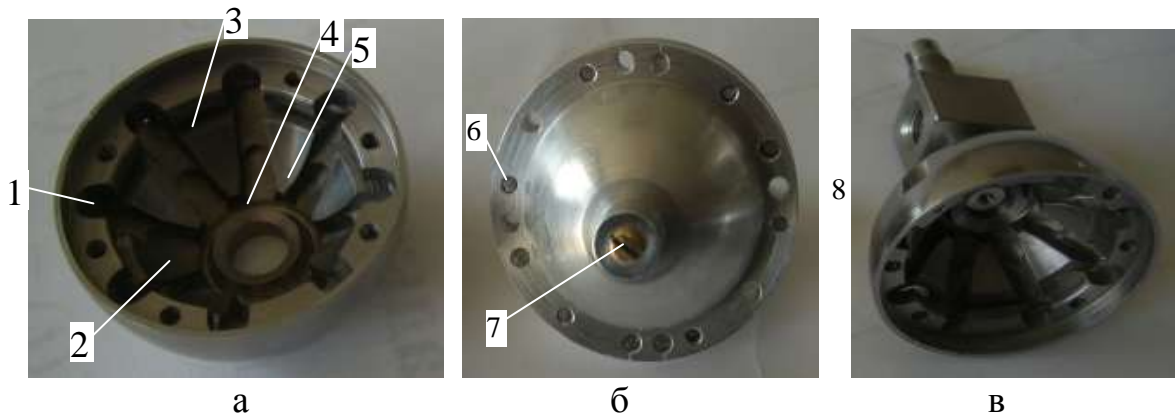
Основні вузли виготовленого демпфера: а – верхня частина обойми; б – корпус із кришкою; в – нижня частина обойми
